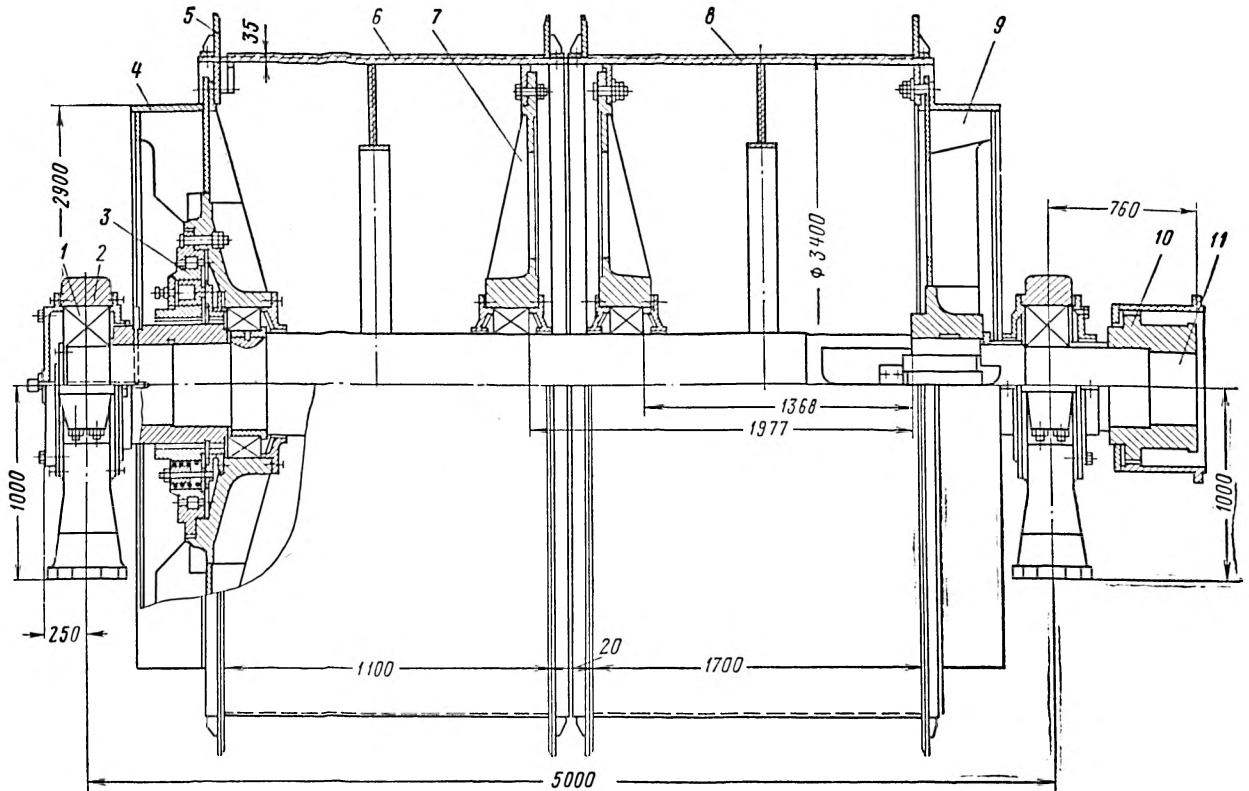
Сборка главного вала машины 2Ц-3,5×1,7А:
